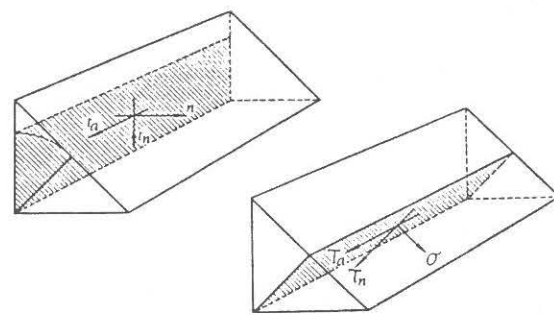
Tensiones en un cordón de soldadura
